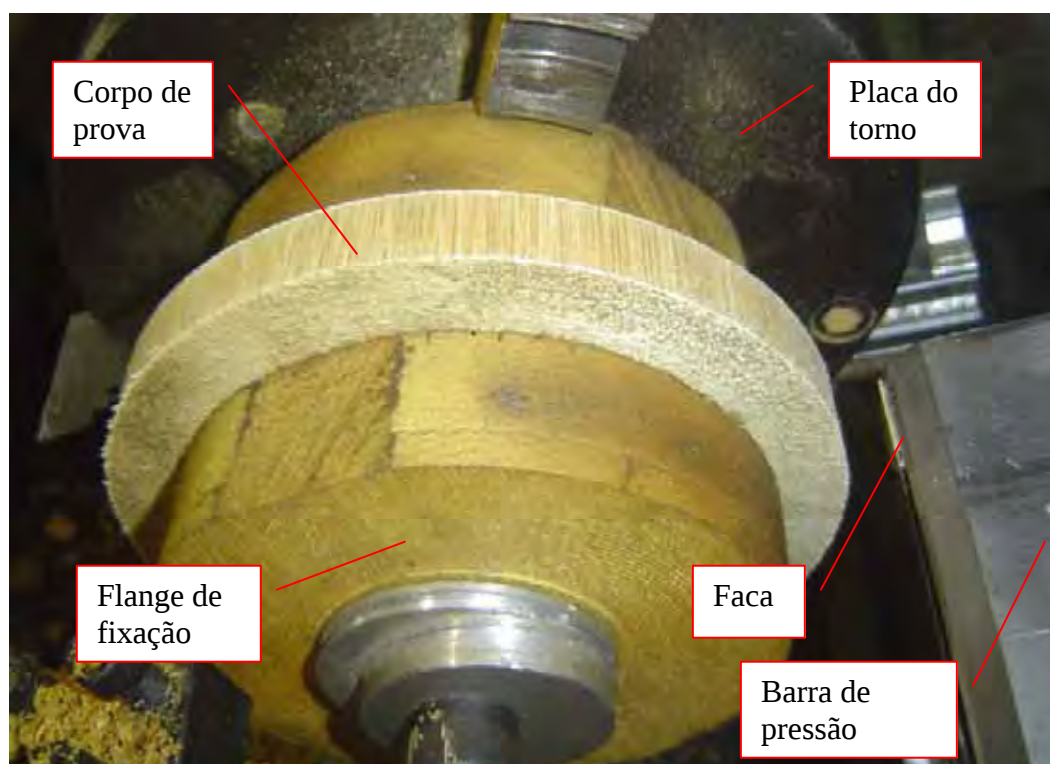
Torno mecânico. Detalhe da faca, barra de pressão e sistema de fixação do corpo de prova.
